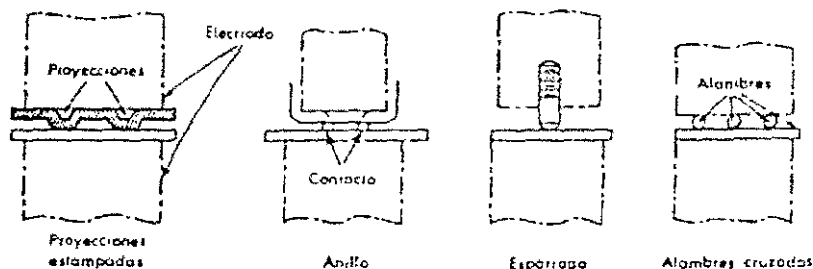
Tipo de soldadura de proyección.
